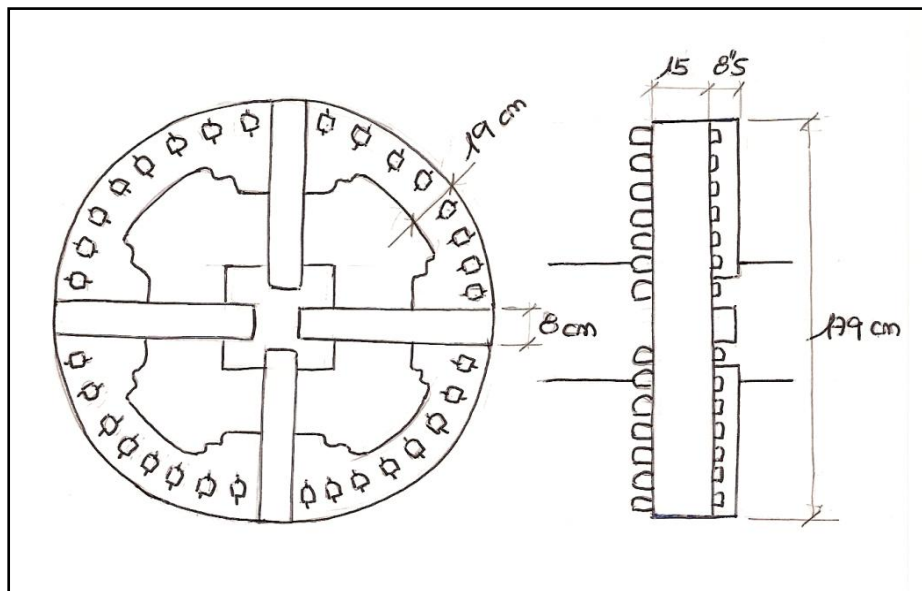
Croquis rueda de engrane con sus principales dimensiones.
